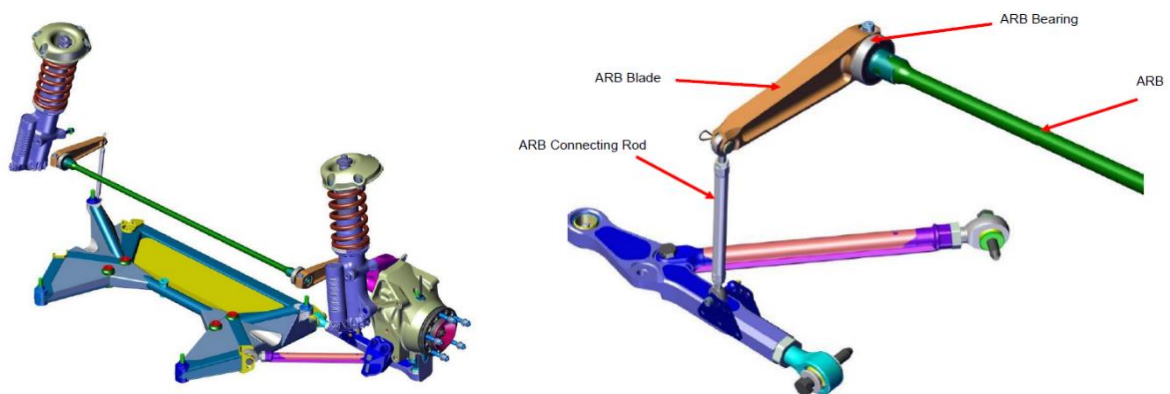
Sistema de amortecimento dianteiro com barra estabilizadora. (Citroën Racing)
